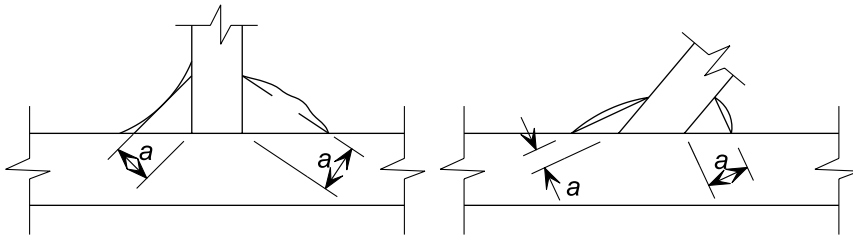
К определению высоты углового сварного шва
